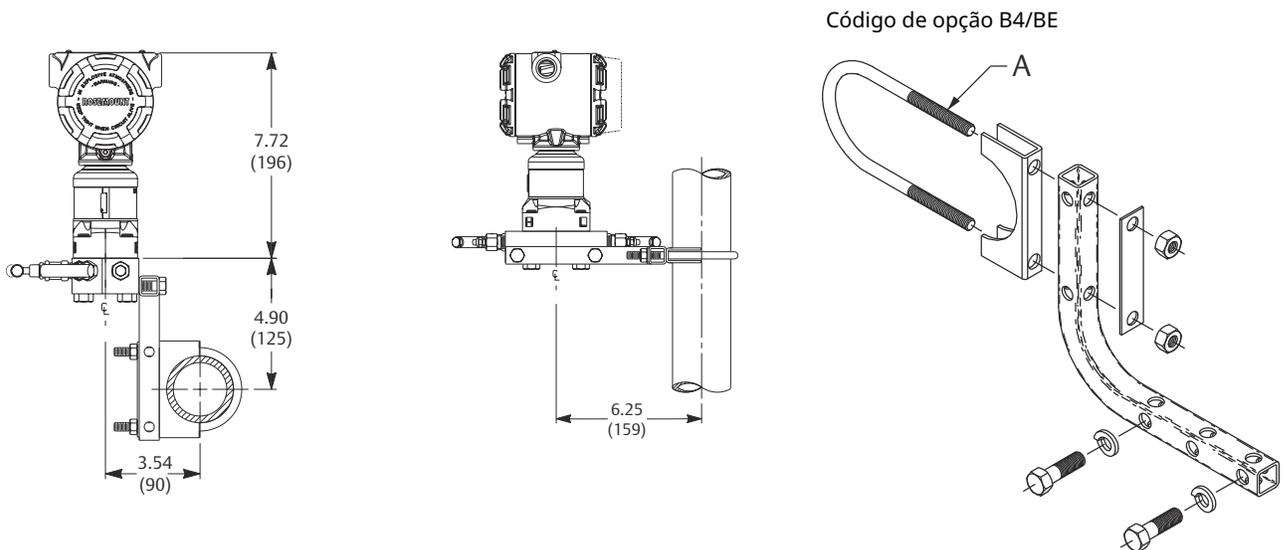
Manifold tradicional com suportes opcionais para montagem em tubo de 2 pol. (50,8 mm)
